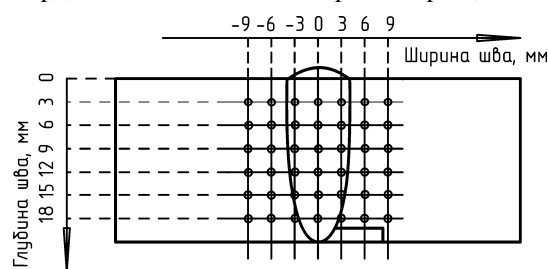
Схема измерения твердости и микротвердости на многослойном сварном образце
